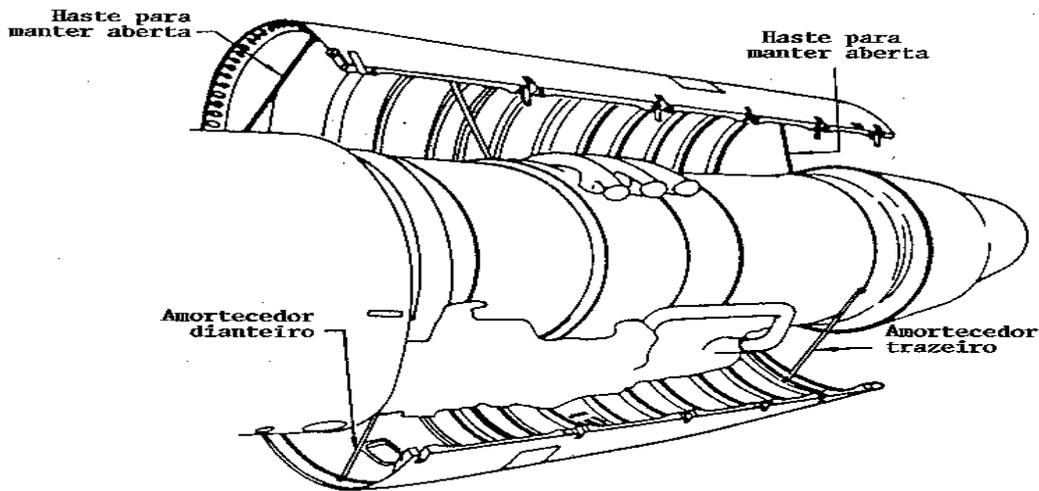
Carenagem de motor a jato com dobradiça lateral.
